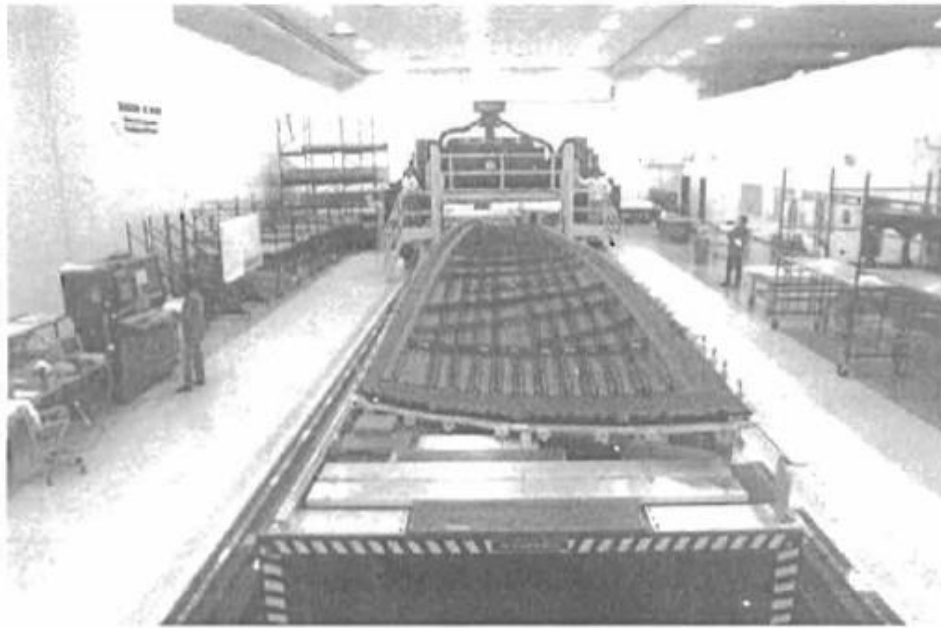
Máquina de coser utilizada para coser alas de material compuesto [21].
